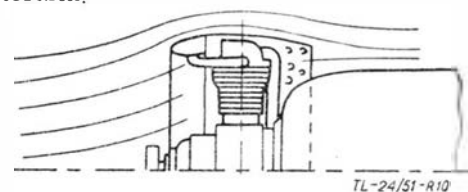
Silnik gwiazdowy z pierścieniem Townenda.
